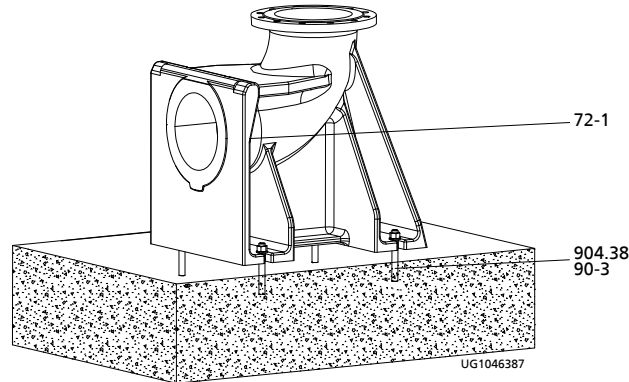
Крепление фланцевого колена с лапой соединительными анкерами
